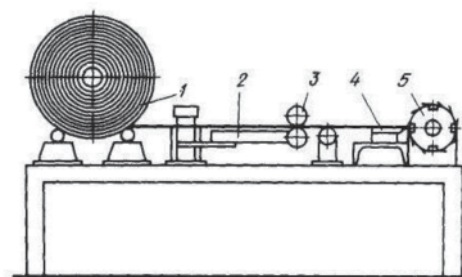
Схема станка для получения фибр из листовой рулонной стали: 1 – рулон листовой стали; 2 – направляющее устройство; 3 – подающий механизм; 4 – неподвижный нож; 5 – ротор с подвижными ножами
